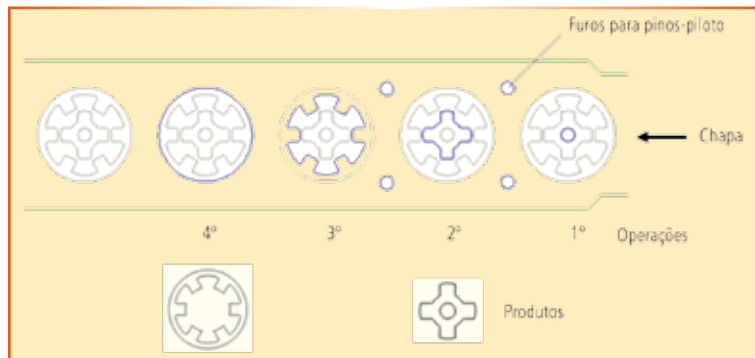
Desenho esquemático da ferramenta de corte em matriz
